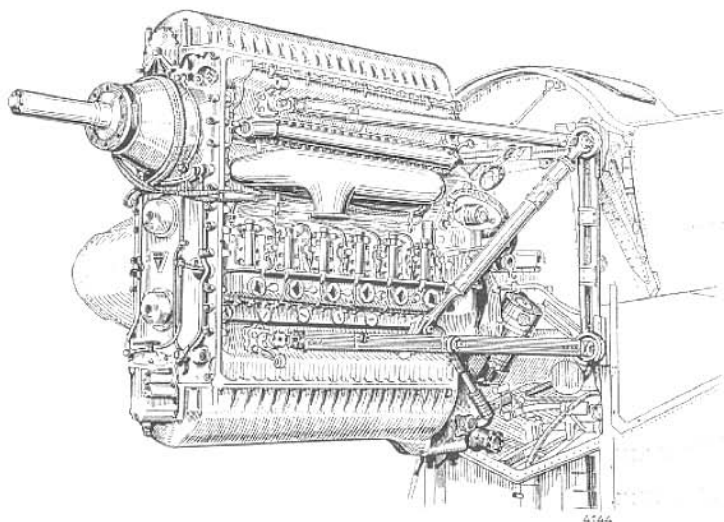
Motoraufhängung JUMO 205 in Ju 86
